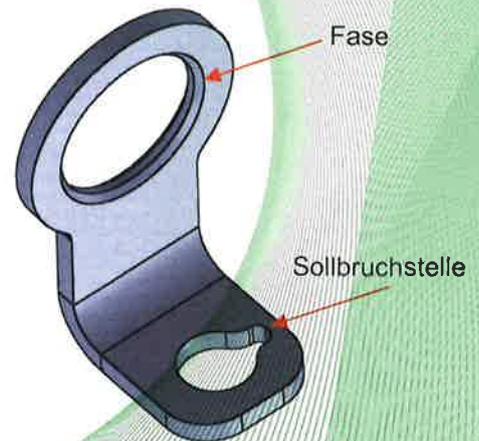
Anschlagpunkt, Typ: TS-Lasche (TS-011) (mit Sollbruchstelle, mit Fasen (1,5 x 45°))
